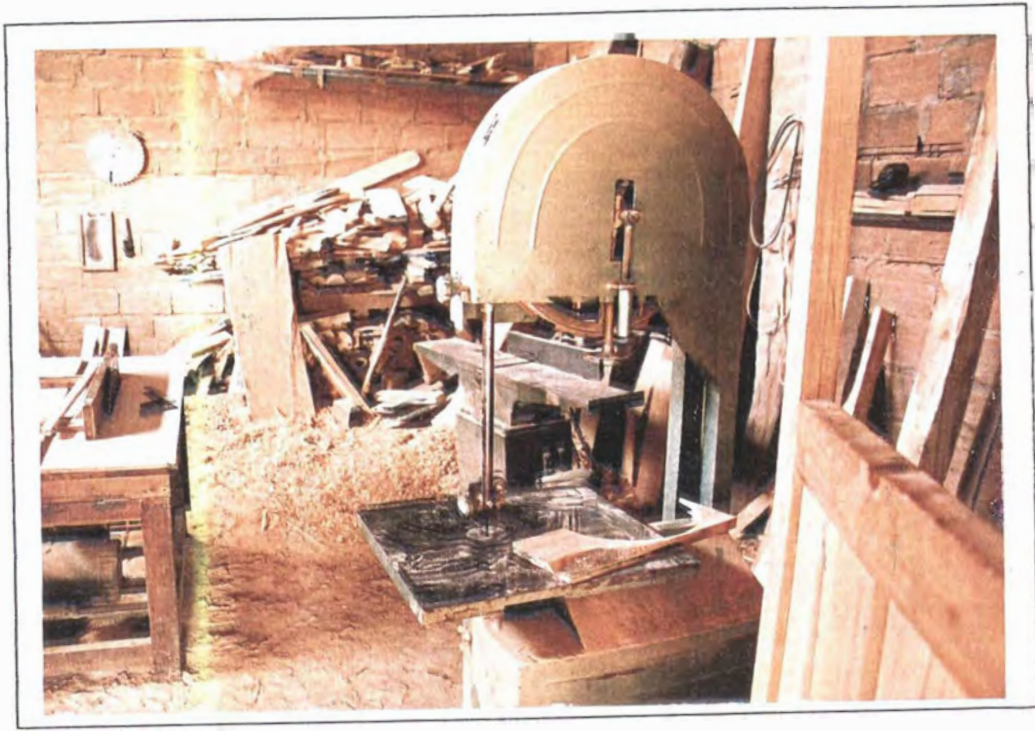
MAQUINAS Y DESECHOS / MUEBLES FERES
